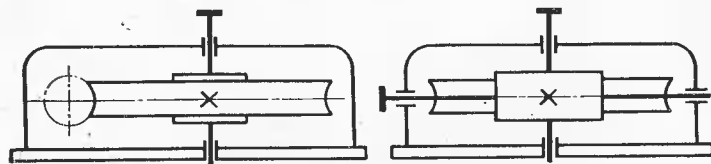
Кинематическая схема червячного редуктора с боковым расположением червяка
